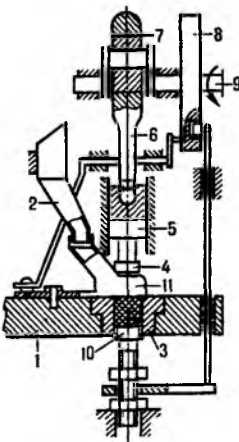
Схема кривошипной таблеточной машины (начало прессования): 1 – стол; 2 – бункер; 3 – матрица; 4 – пуансон; 5 – ползунок; 6 – шатун; 7, 8 – эксцентрики; 9 – коленчатый вал; 10 – выталкиватель; 11 – загрузочное устройство.
